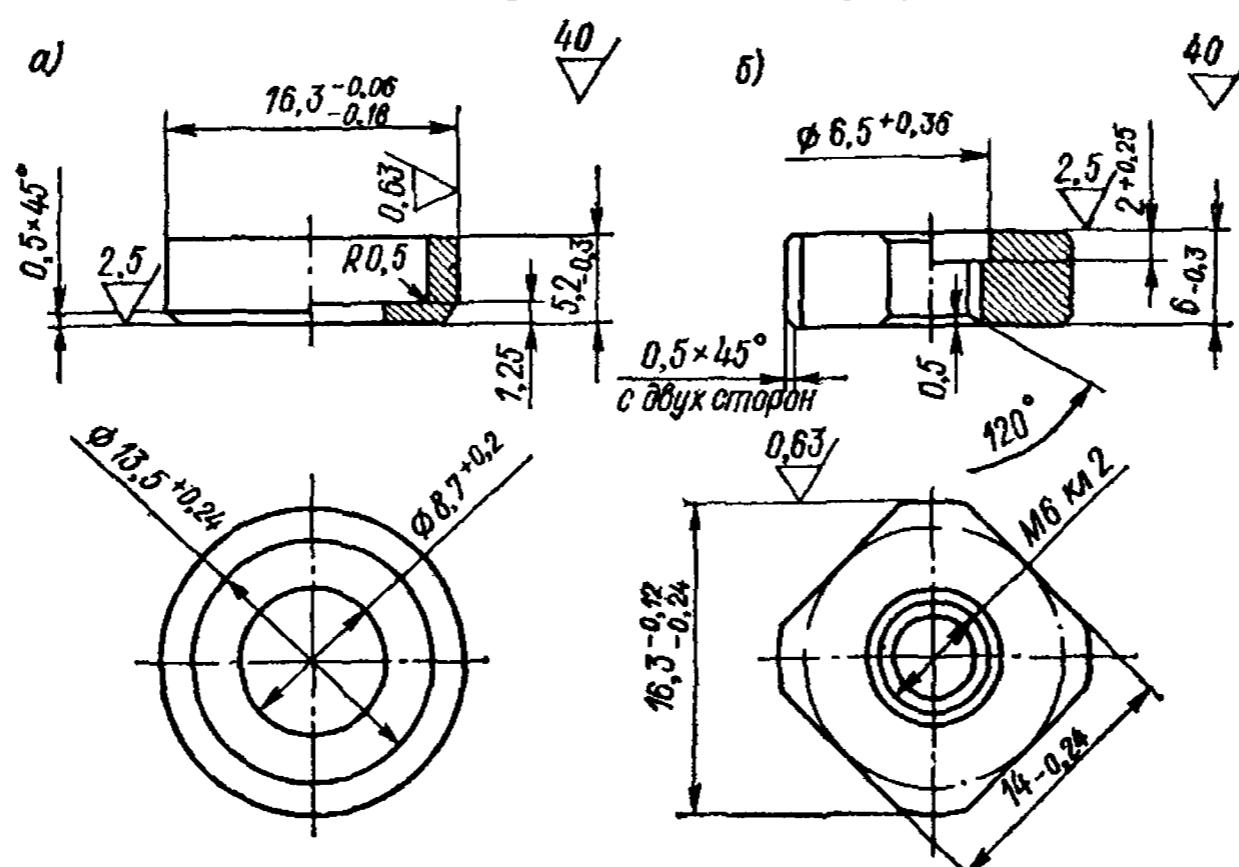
Ремонтные детали амортизатора: а — поршень; б — направляющая
